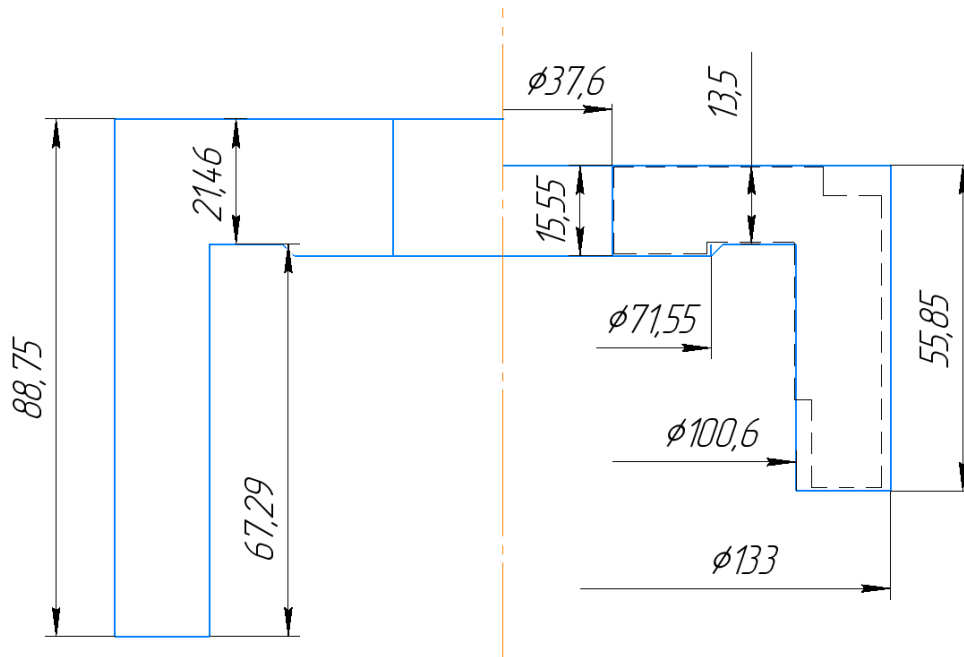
Размеры заготовки перед спеканием и размеры объема засыпки порошка в пресс-форму.
